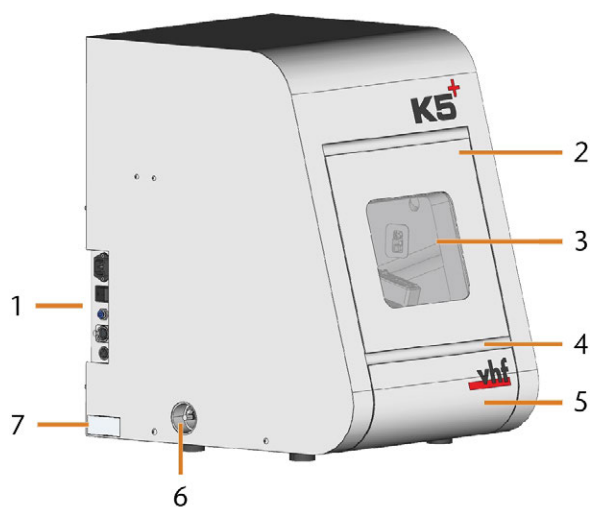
VISTA FRONTAL DE LA MÁQUINA
